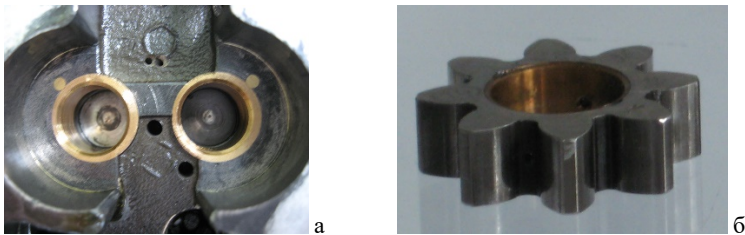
Поверхні тертя робочих деталей НШ (виріб 623АНМ).
